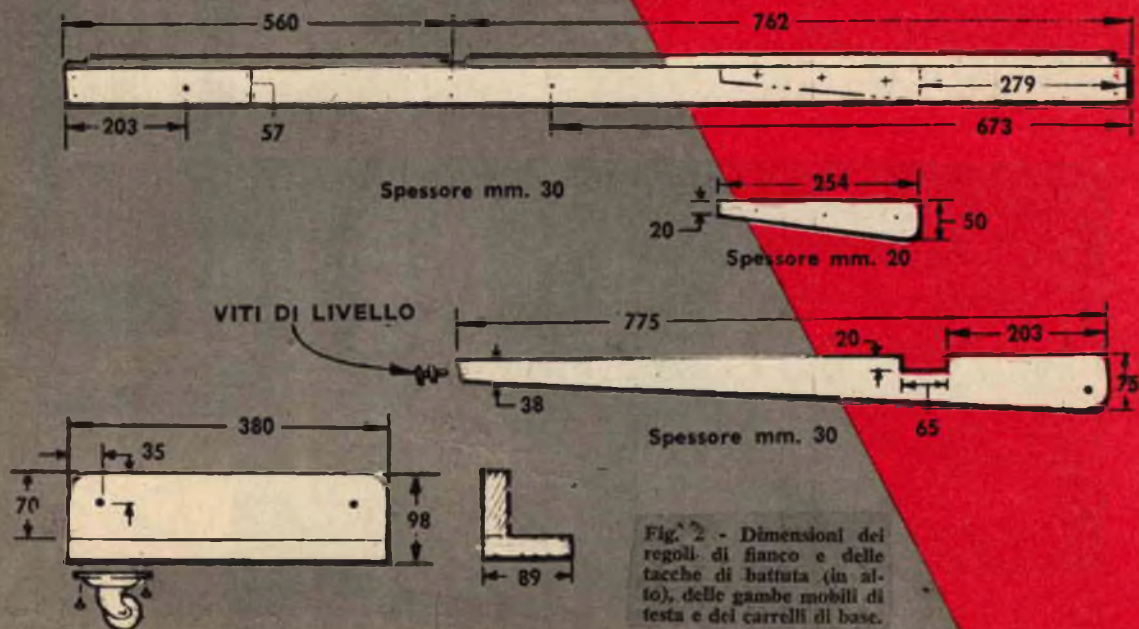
Dimensioni dei regoli di fianco e delle tacche di battuta (in alto), delle gambe mobili di testa e dei carrelli di base.
